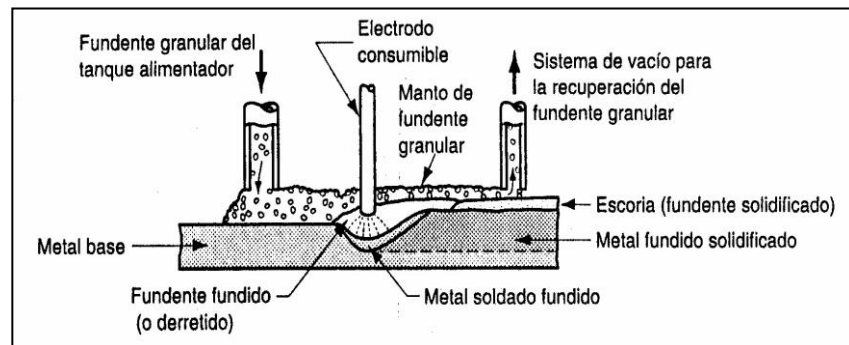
SOLDADURA CON ARCO SUMERGIDO
